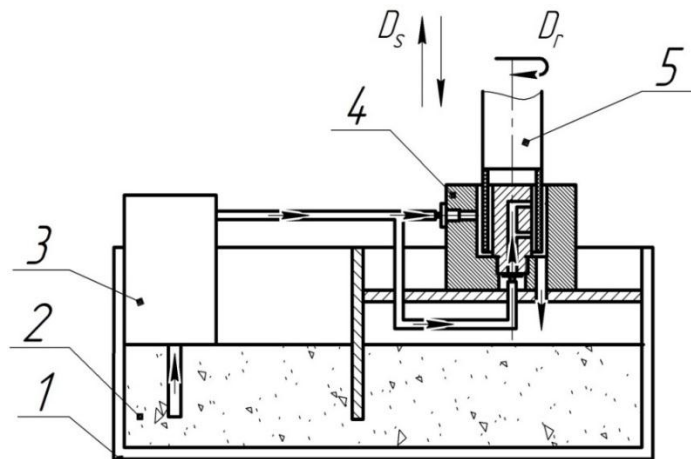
Схема правки свободным абразивом кольцевого алмазного сверла с подачей в виде суспензии
